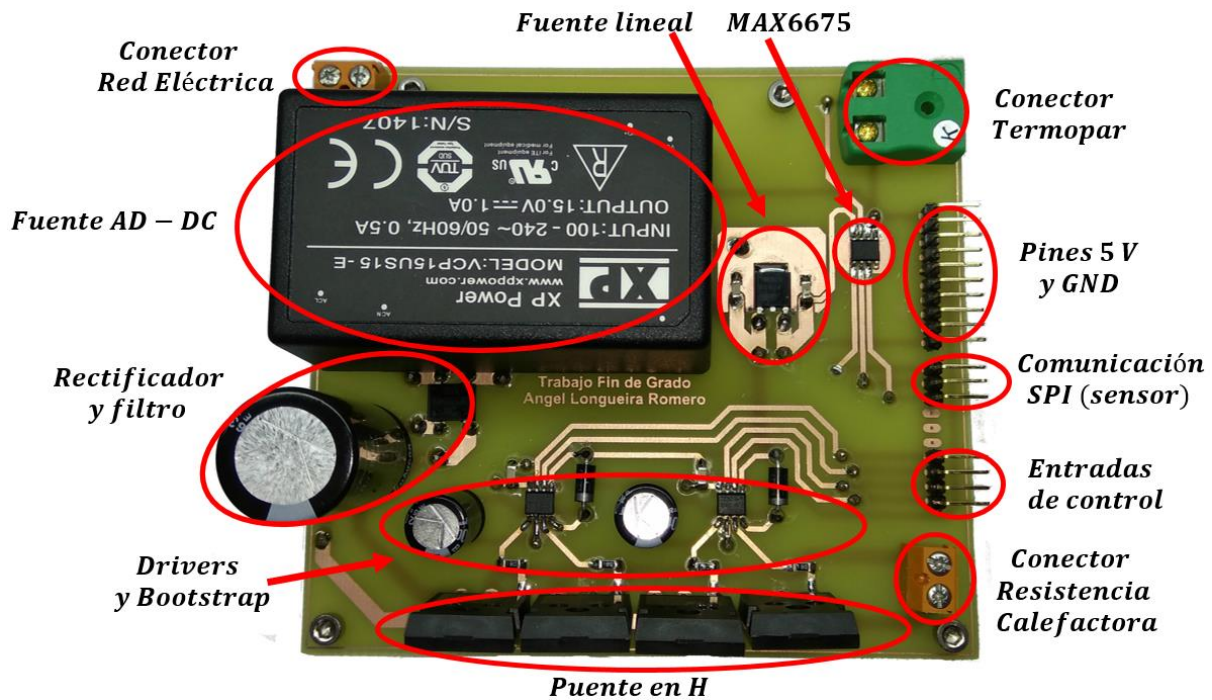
Cara superior (*top layer*) de la PCB.
